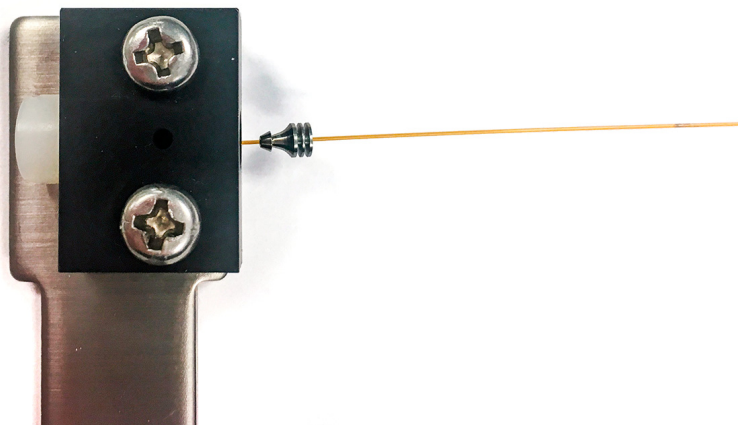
Einschrauben der Mutter in das Einwalzwerkzeug
